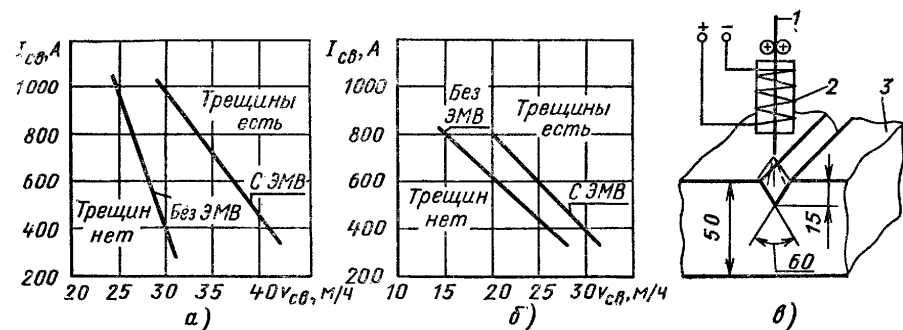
Влияние скорости сварки, силы тока и электромагнитного поля (ЭМВ) на появление горячих трещин при сварке под флюсом образцов жесткой пробы № 1 (см. рис. 12) из хромоникельмолибденовой стали:
